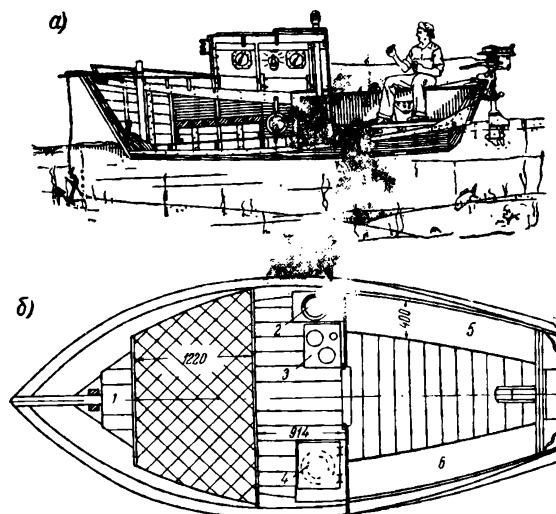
Маленький туристский катер необычной конструкции с подвесным мотором: а — продольный разрез; б — план.
